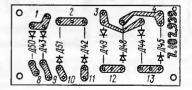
Схема расположения установочных элементов (вид сооку) Fig. 7. Layout of Adjustment Elements (Side View)
